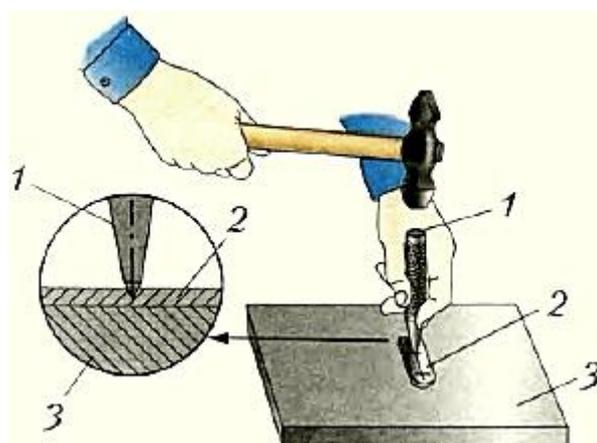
Накернивание центров будущих отверстий: 1 — кернер; 2 — заготовка; 3 — металлическая плита
